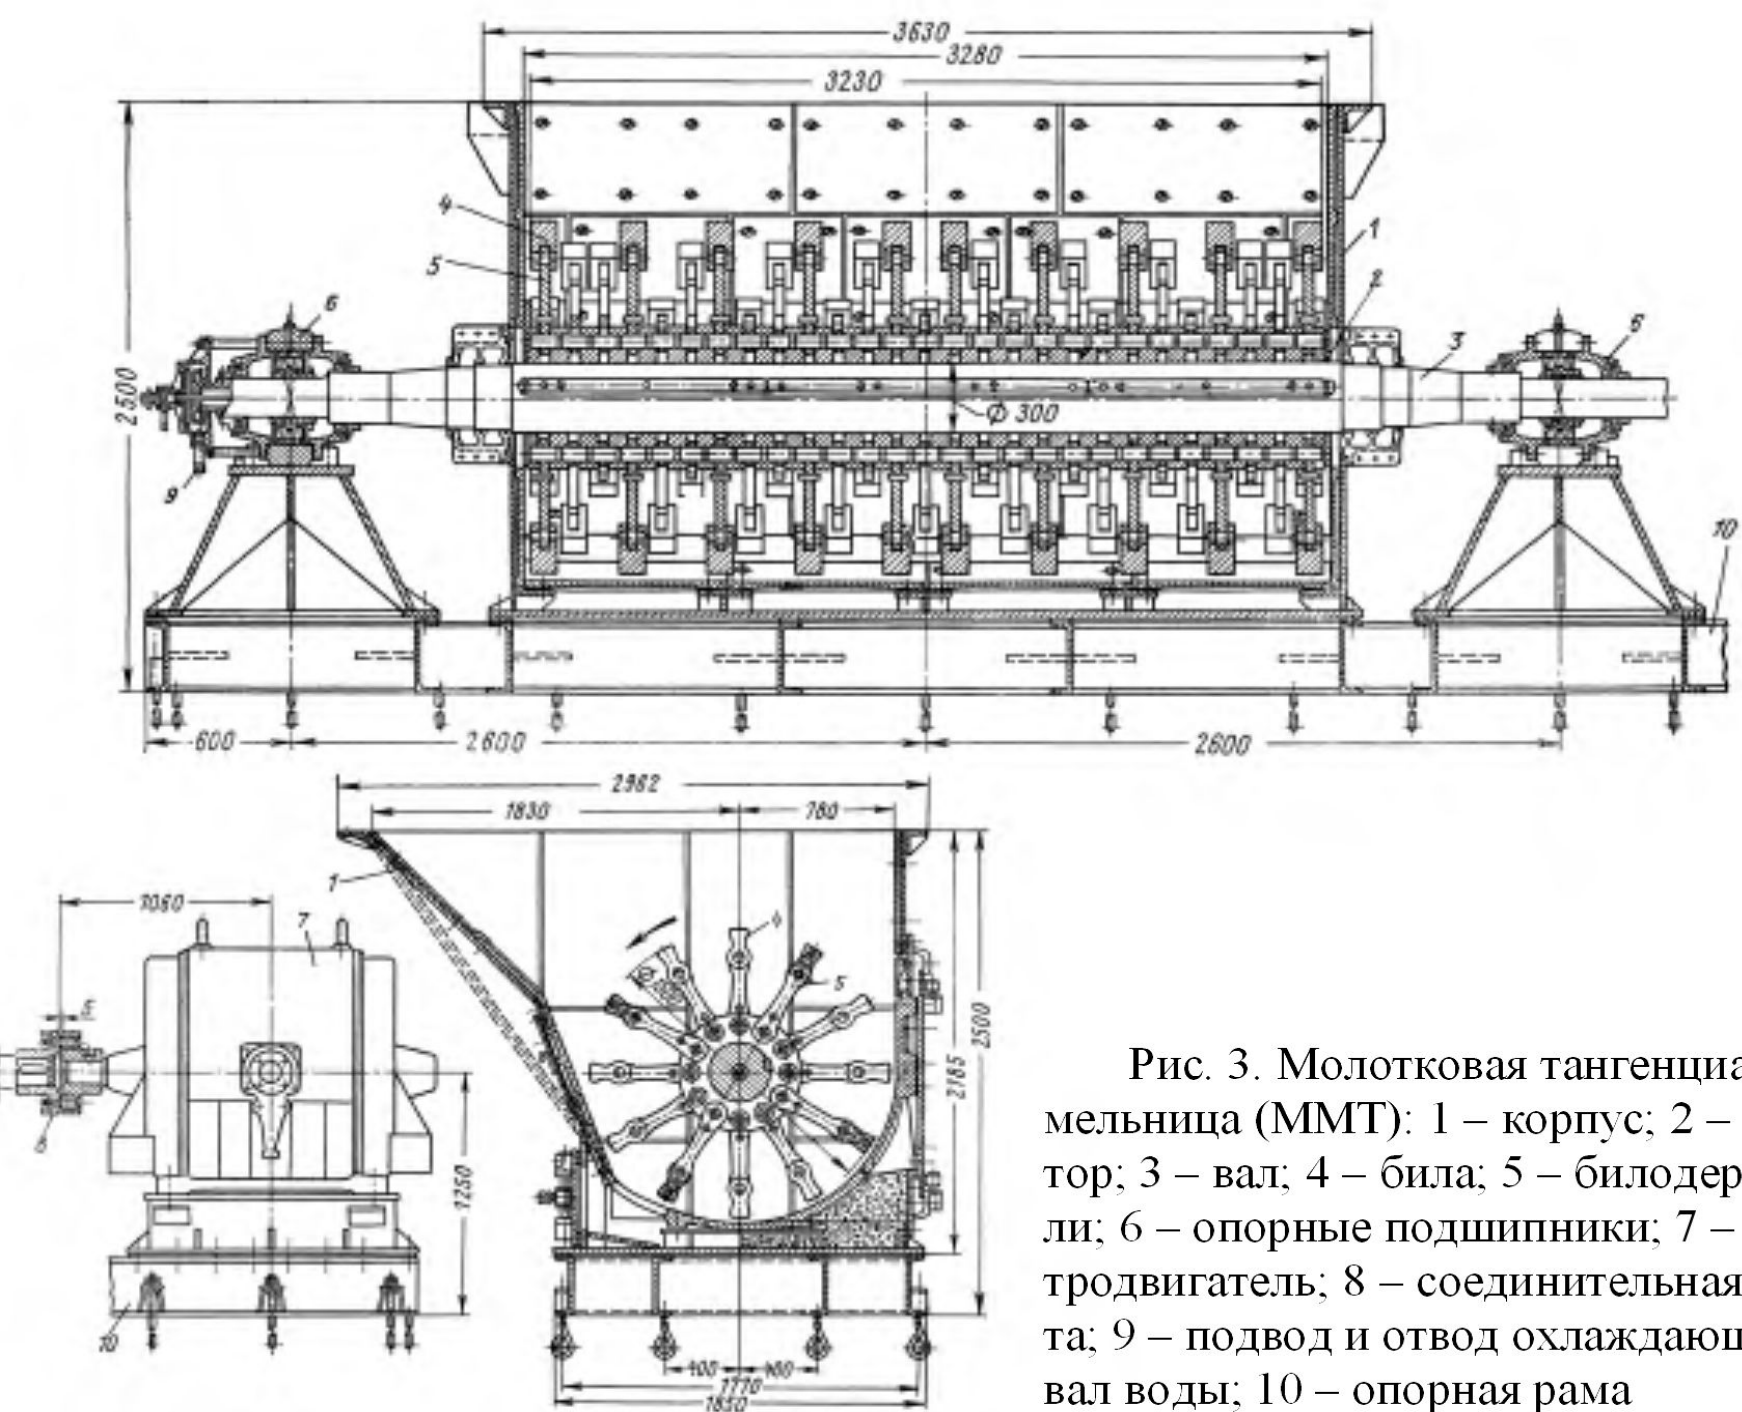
Молотковая тангенциальная мельница (ММТ): 1 – корпус; 2 – ротор; 3 – вал; 4 – била; 5 – билодержатели; 6 – опорные подшипники; 7 – электродвигатель; 8 – соединительная муфта; 9 – подвод и отвод охлаждающей вал воды; 10 – опорная рама
